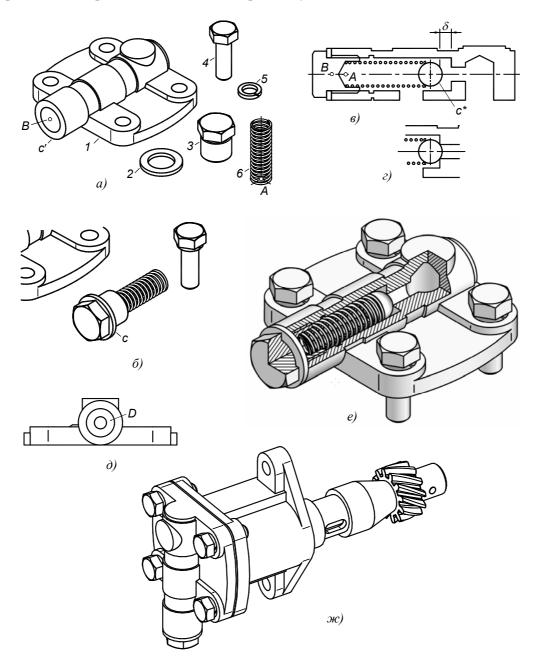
Крышка в сборе: a – загрузка моделей; δ – предварительная сборка и координирование; ϵ , ϵ , ϵ , ϵ – сборка и корректировка перепускного клапана;
